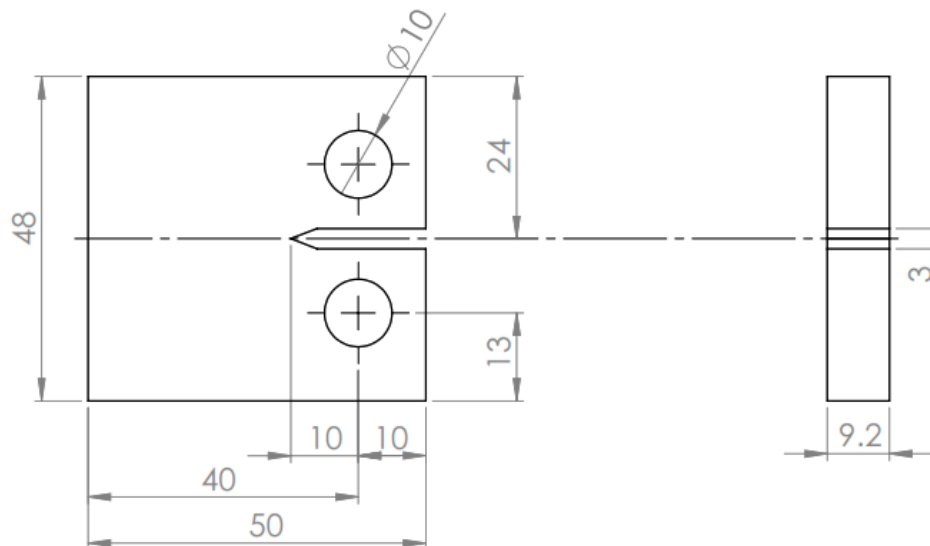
Dimensiones de probeta de tensión compacta (CT) en mm.
